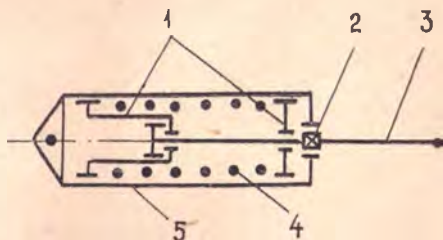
Схема взлетно-посадочного загрузателя: 1 — плунжер; 2 — упор штока; 3 — шток; 4 — пружина; 5 — цилиндр
